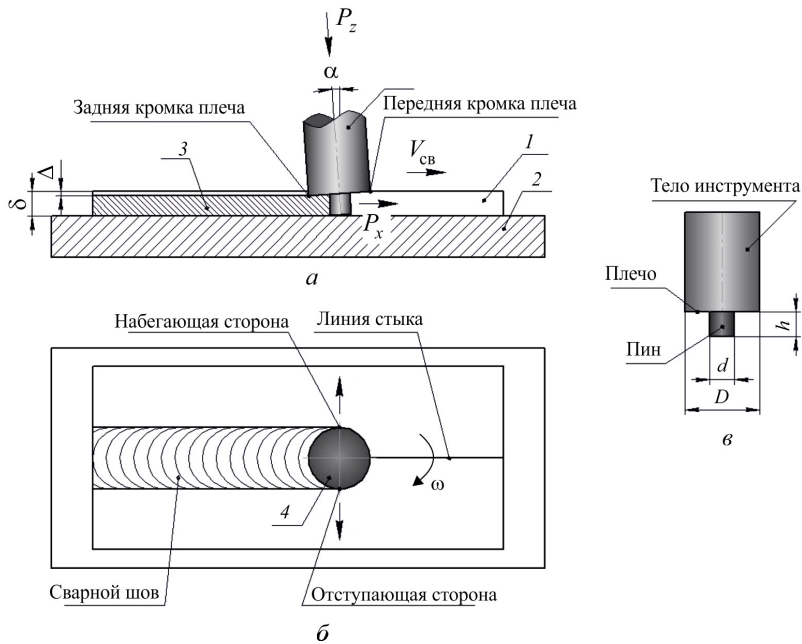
Схема усилий при сварке трением с перемешиванием: *a* – сечение по линии стыка; *б* – вид сверху; *в* – общая схема инструмента для СТП; 1 – свариваемые пластины; 2 – подложка; 3 – сварной шов; 4 – инструмент;  $\alpha$  – угол наклона инструмента;  $V_{св}$  – скорость сварки;  $\delta$  – толщина свариваемых пластин;  $\Delta$  – глубина погружения инструмента;  $\omega$  – скорость вращения инструмента;  $P_z$  – осевое усилие;  $P_x$  – продольное усилие
